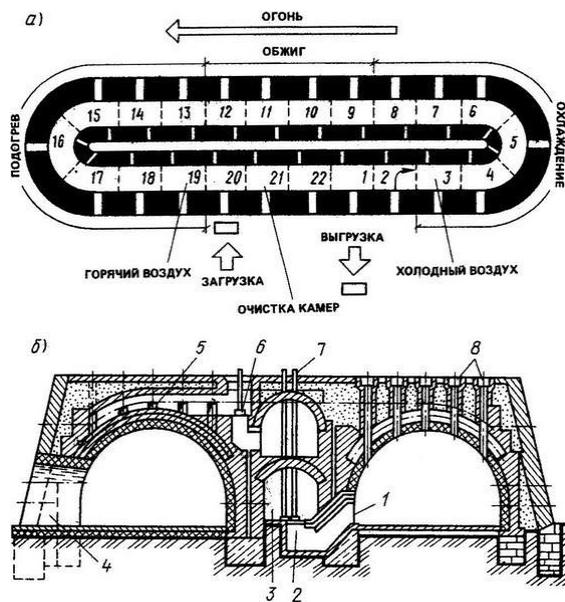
Схема работы (а) и разрез (б) кольцевой печи: 1 – дымовые очелки; 2 – дымовой конус; 3 – дымовой канал; 4 – ходок; 5 – рассыпной строй; 6 – клапан рассыпного строя; 7 – штанга; 8 – топливные отверстия
